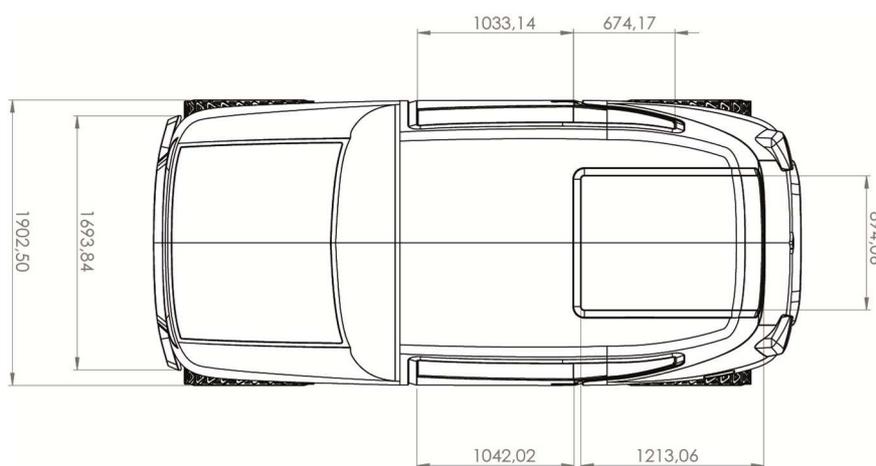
Vista superior. Escala 1/50; dimensões em milímetros. Fonte: autor.
